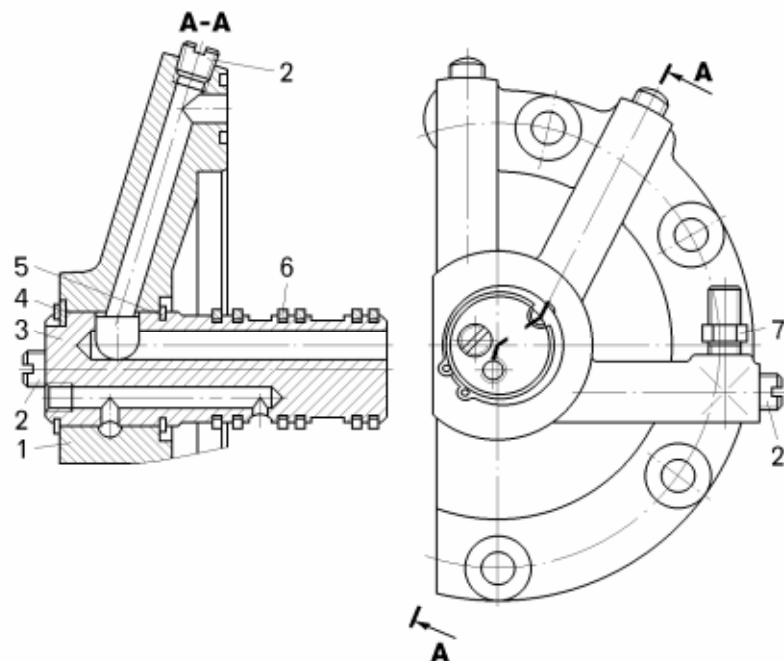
Крышка реверсивного вала с распределителем:
